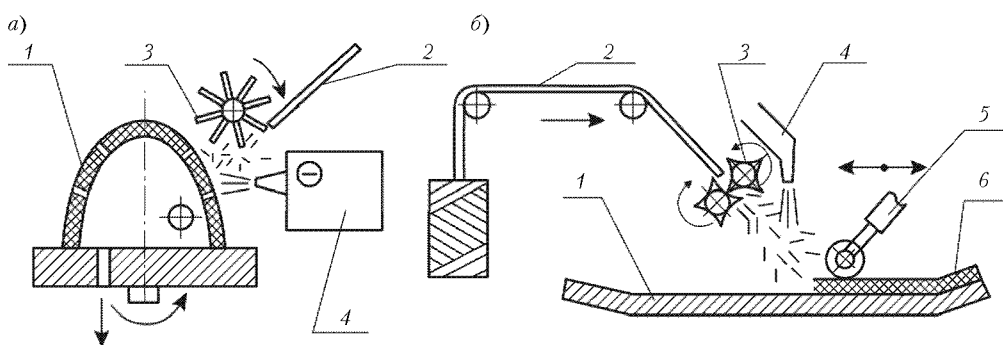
Схема нанесения покрытий напылением: а — электроосаждение; б — уплотнение прикатным валиком; 1 — форма; 2 — ровинг; 3 — рубильное устройство; 4 — форсунки со связующим; 5 — прикатной валик; 6 — уплотненный слой ПКМ
